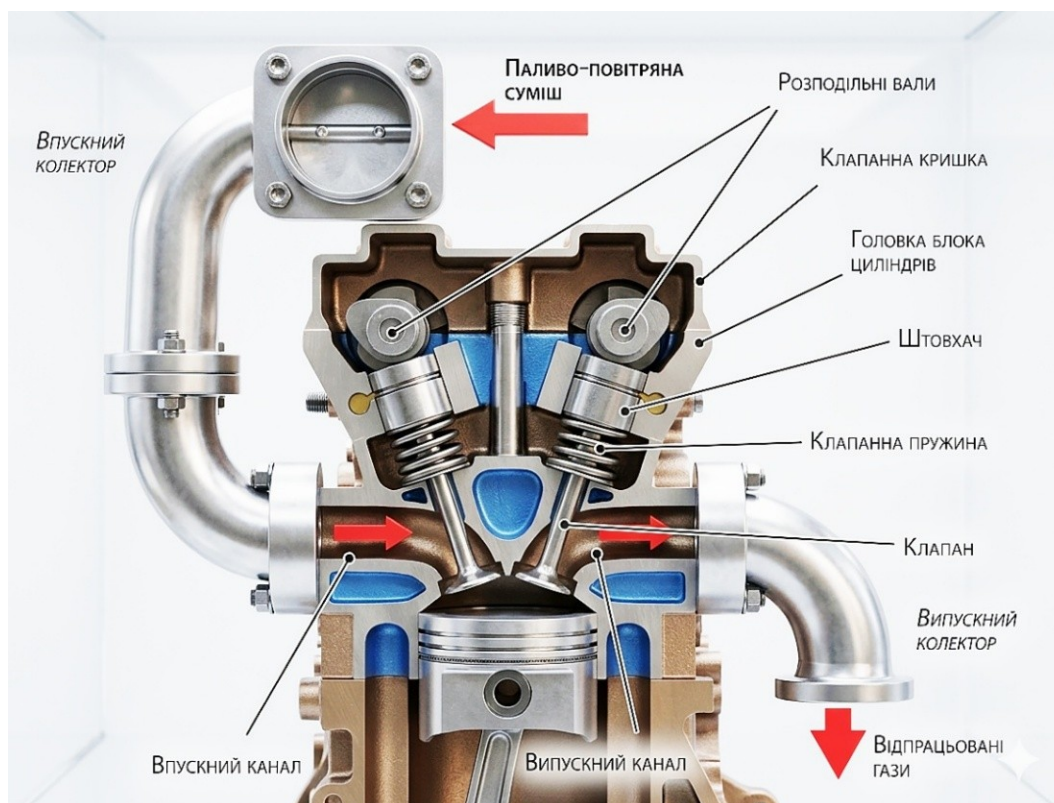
Головка блока циліндрів із газорозподільним механізмом.
